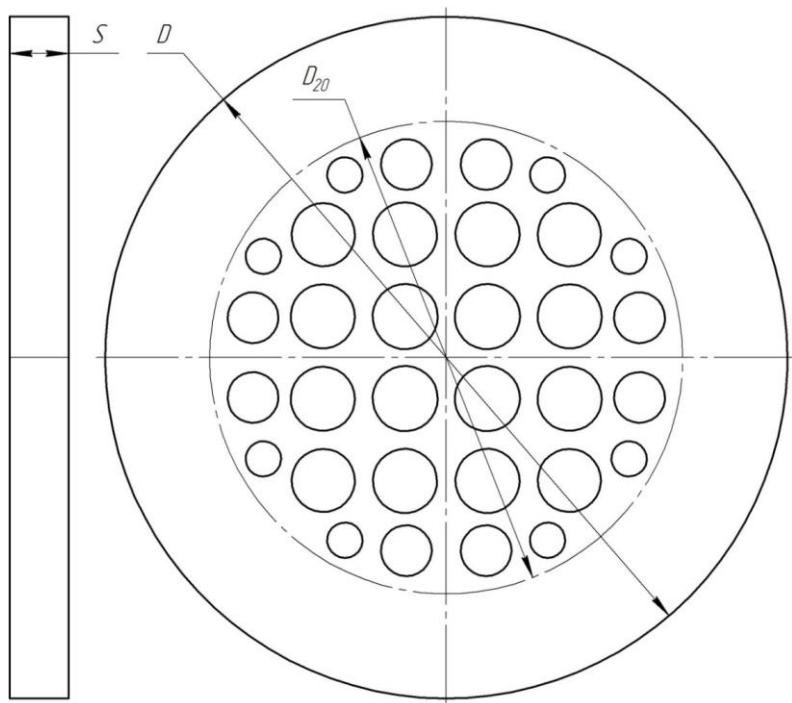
Габаритно-присоединительные размеры диска УПП-Д
